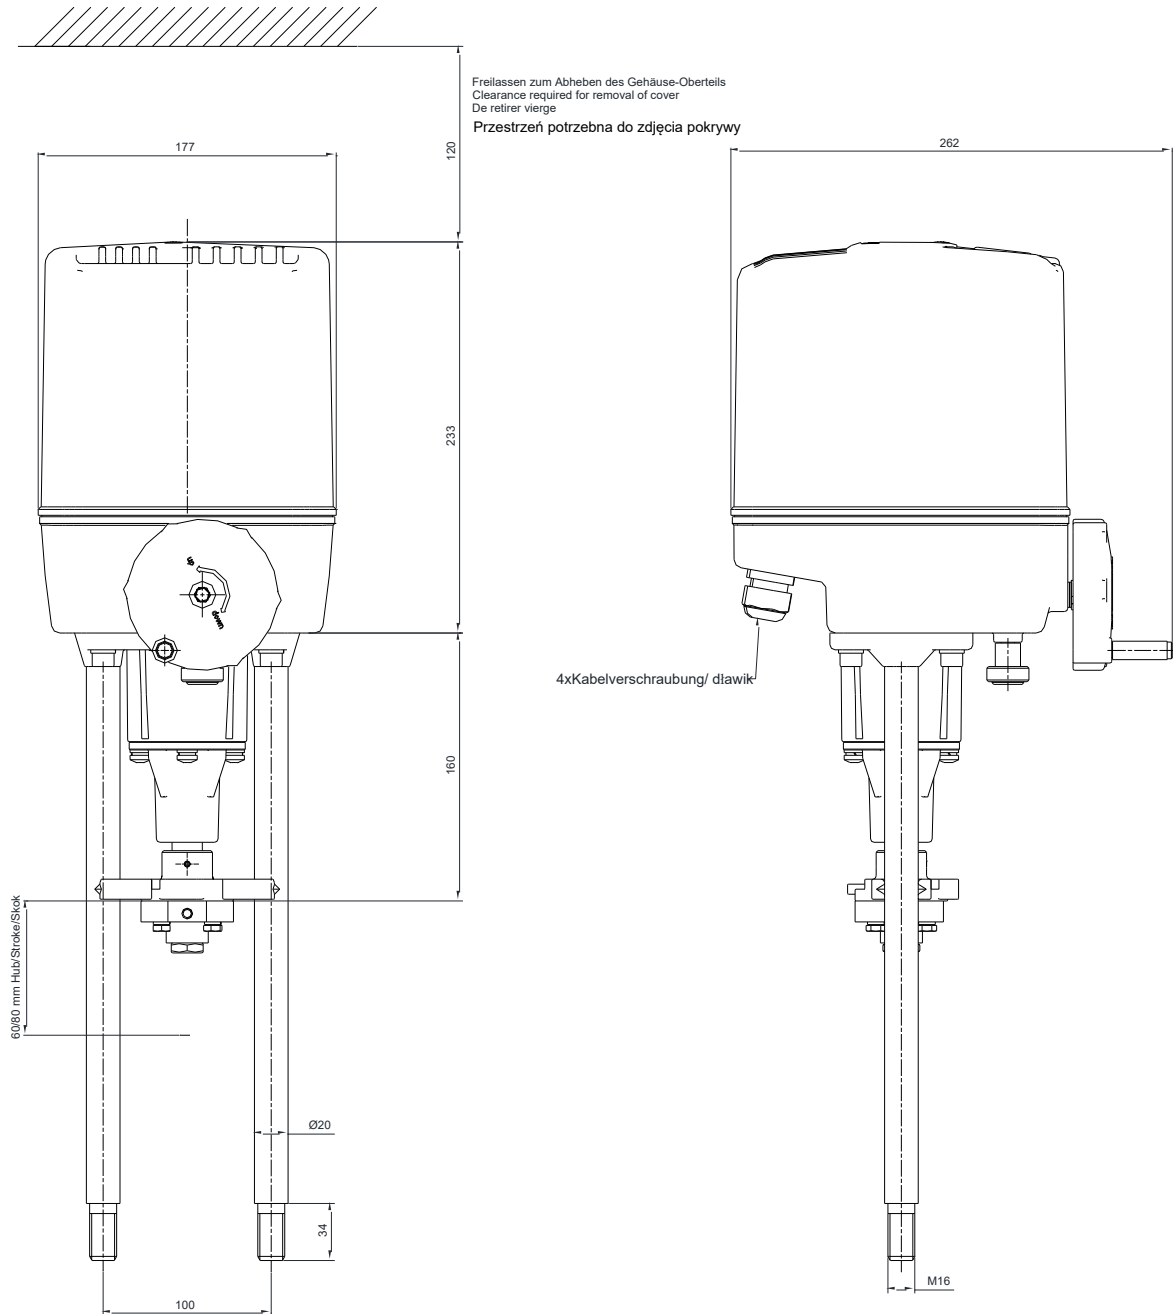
Maßblatt/Dimension sheet/wymiary
